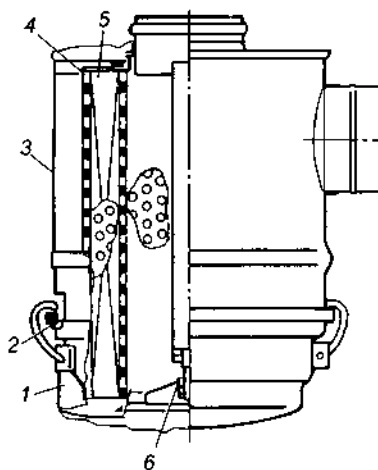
Воздушный фильтр: 1 — крышка; 2 — прокладка; 3 — корпус; 4 — пылеотбойник; 5 — фильтрующий элемент; 6 — гайка
